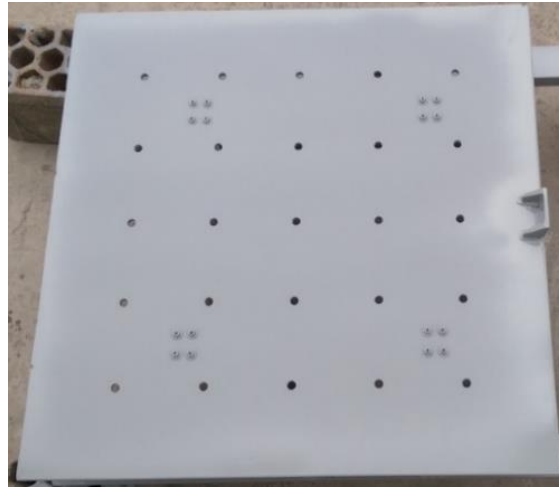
Vista de planta de la plataforma de Acero A – 36
